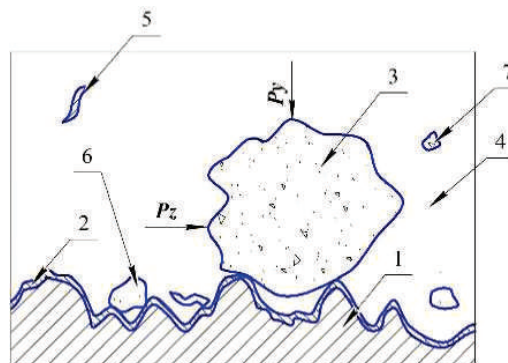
Контактные взаимодействия единичного абразивного зерна с поверхностью лопатки: 1 – микровыступ лопатки; 2 – окисленный слой; 3 – абразивное зерно; 4 – полимерная основа РС; 5 – стружка; 6 – мелкое абразивное зерно; 7 – осколки
